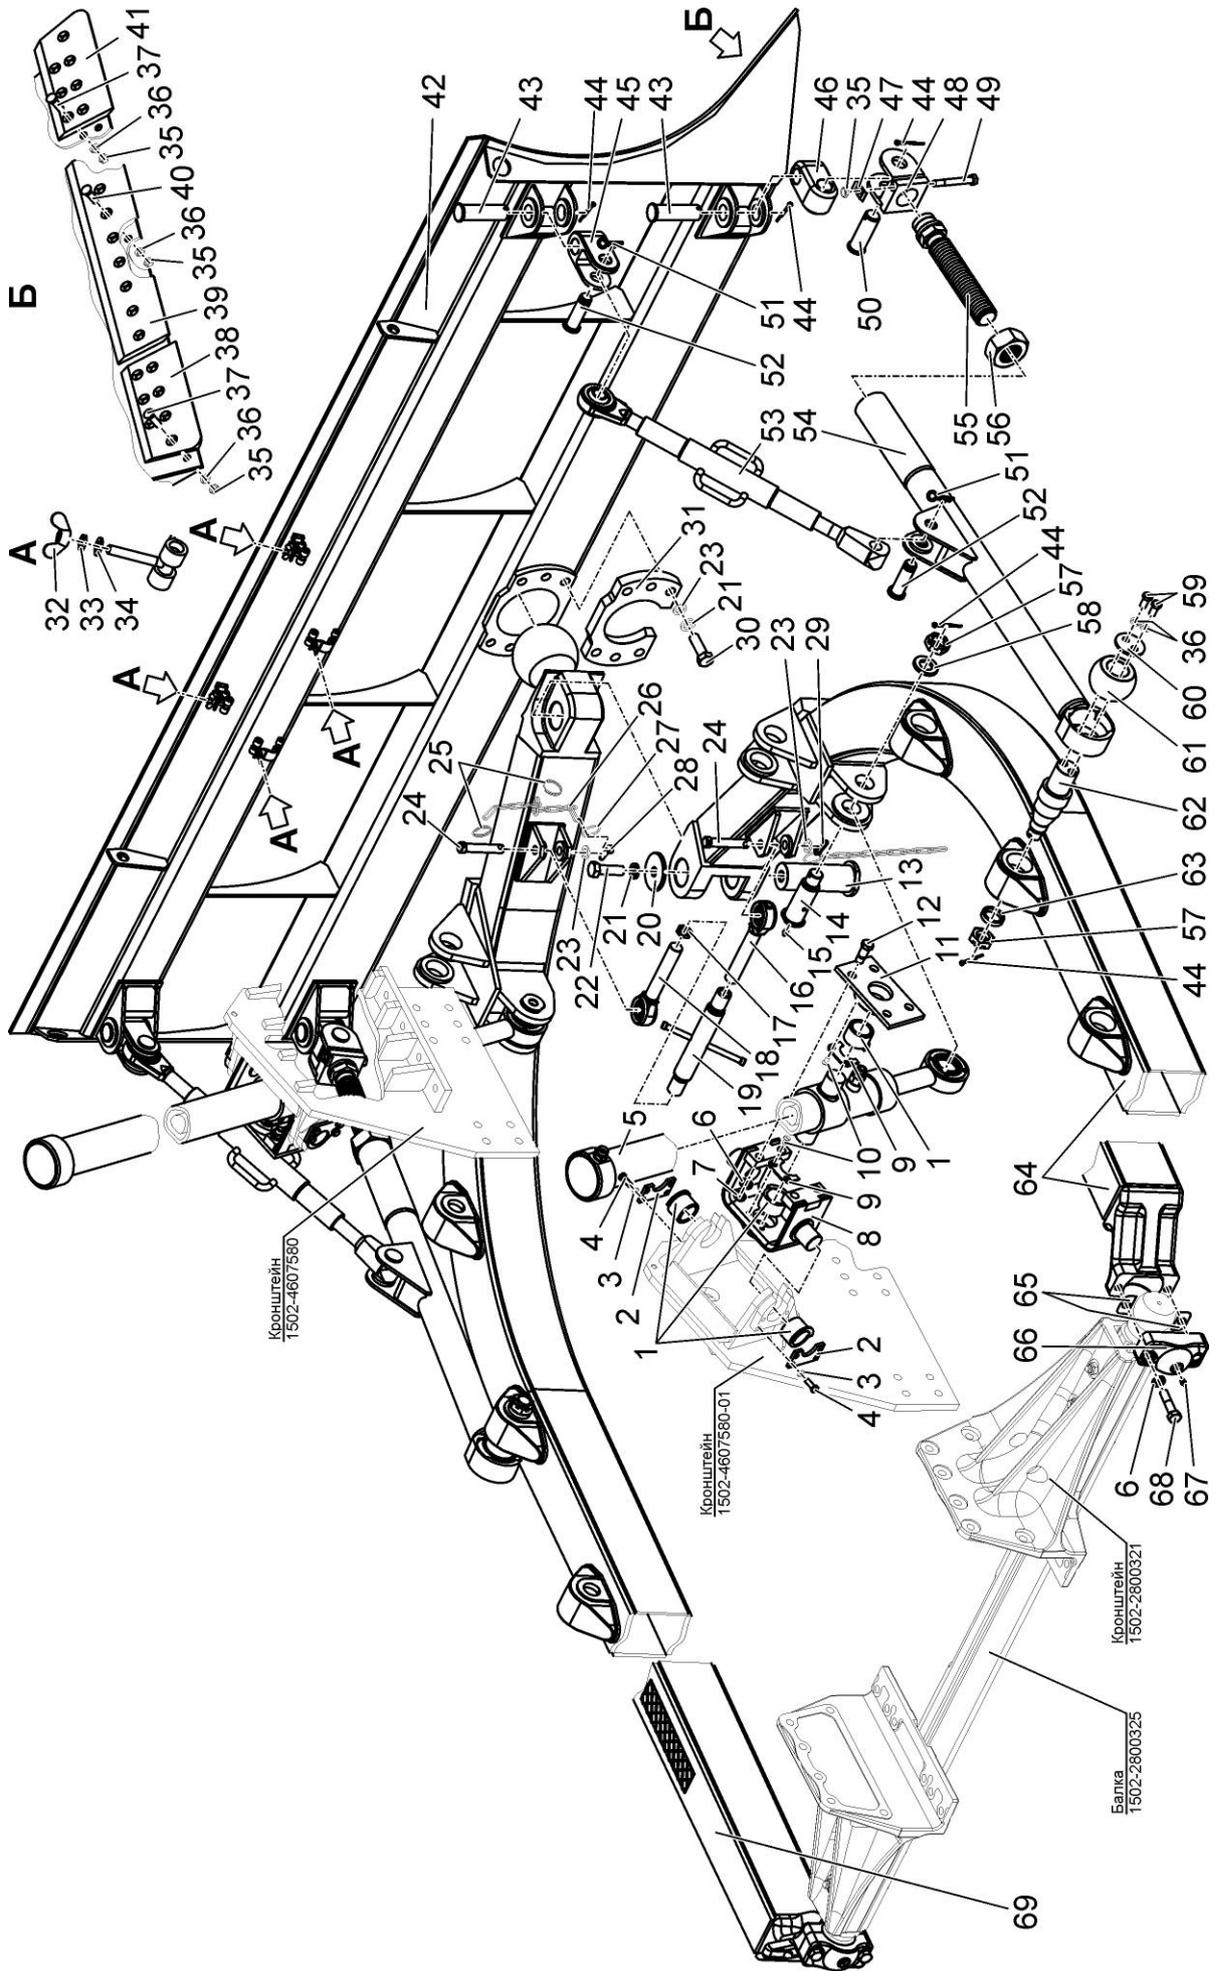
Установка отвала. Вилка. Тяга верхняя. Винт
